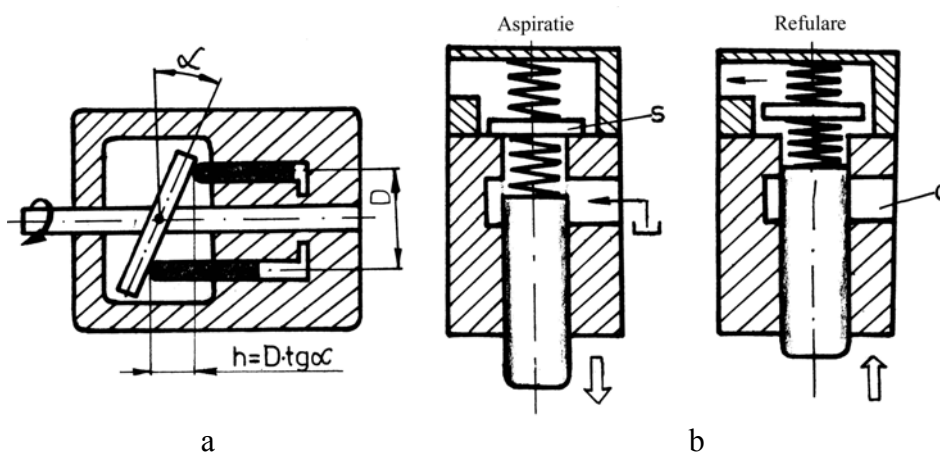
Schița pompei cu pistonăse axiale cu disc fulant.
